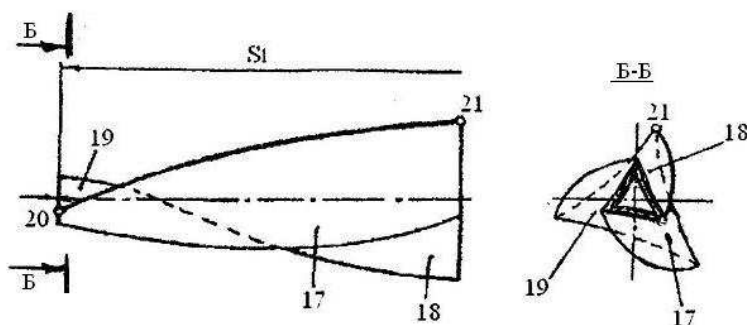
Часть корпуса вращающейся печи для приготовления цементного клинкера с тремя винтовыми ребрами (17, 18 и 19- трапециевидные листы, 20-21- одно из трех винтовых ребер)
